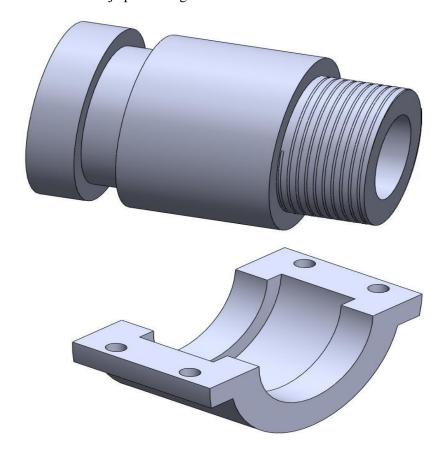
Cabezal diseñado a partir de programa CAD Solidworks, C. Jiménez.
